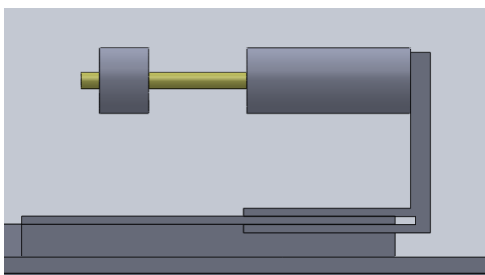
Pormenor do suporte do rolo de etiquetas.
